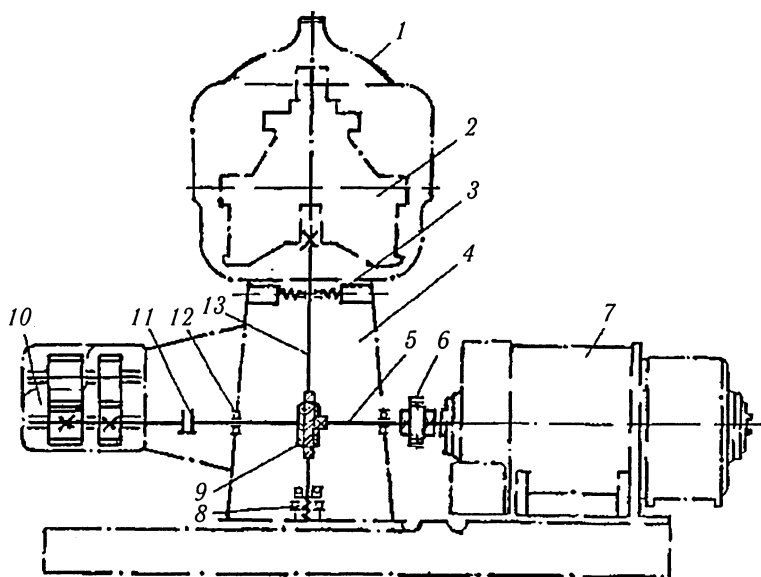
Принципиальная кинематическая схема сепаратора: 1 — сборник; 2 — барабан; 3 — верхняя опора; 4 — станина; 5 — горизонтальный вал; 6 — фрикционная муфта; 7 — электродвигатель; 8 — нижняя опора; 9 — червячно-винтовая пара; 10 — шестеренные насосы; 11 — эластичная муфта; 12 — подшипник; 13 — вертикальный вал
